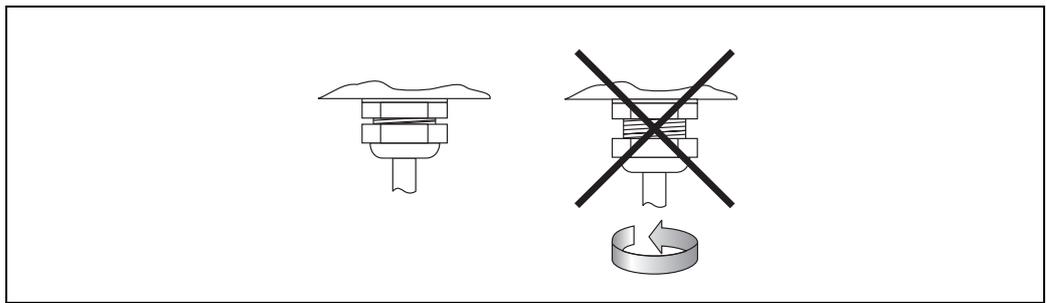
Instrucciones de instalación referentes a las entradas de cables de la caja del transmisor
